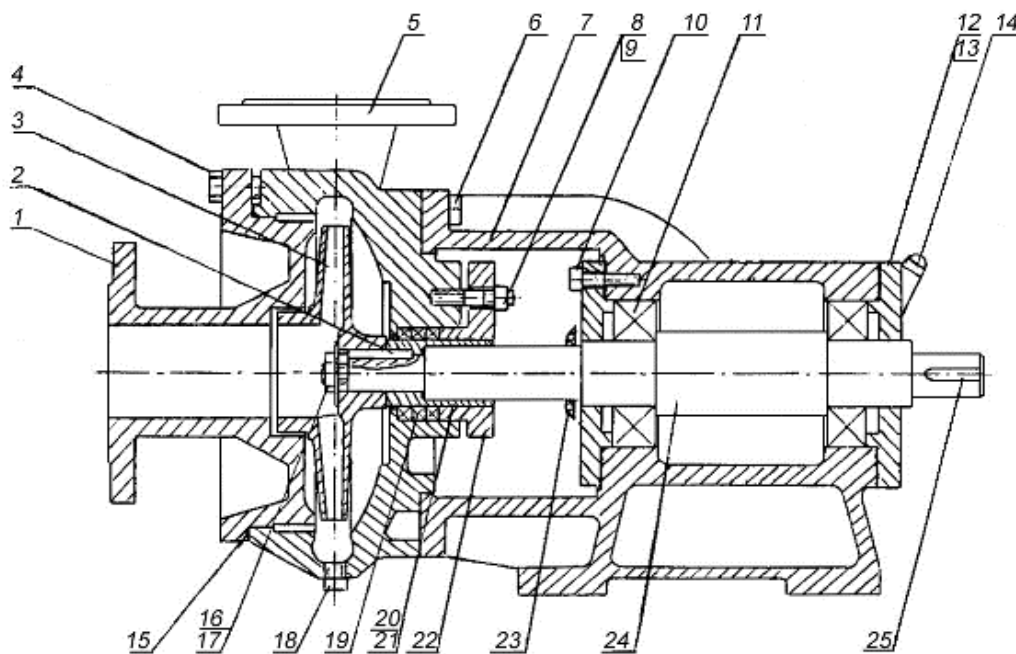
Конструкция насоса типа 2К: 1 - крышка насоса; 2 - шпонка; 3 - рабочее колесо; 4.6 - болт; 5 - корпус насоса; 7 - корпус подшипников; 8 - гайка; 9 - шпилька; 10 - болт; 11 - подшипник; 12 - крышка подшипника; 13 - прокладка; 14 - масленка; 15 - прокладка; 16 - гайка рабочего колеса; 17 - шайба; 18 - пробка; 19 - набивка сальниковая; 20 - втулка защитная; 21 - прокладка; 22 - крышка сальника; 23 - отбойник; 24 - вал; 25 - шпонка.
